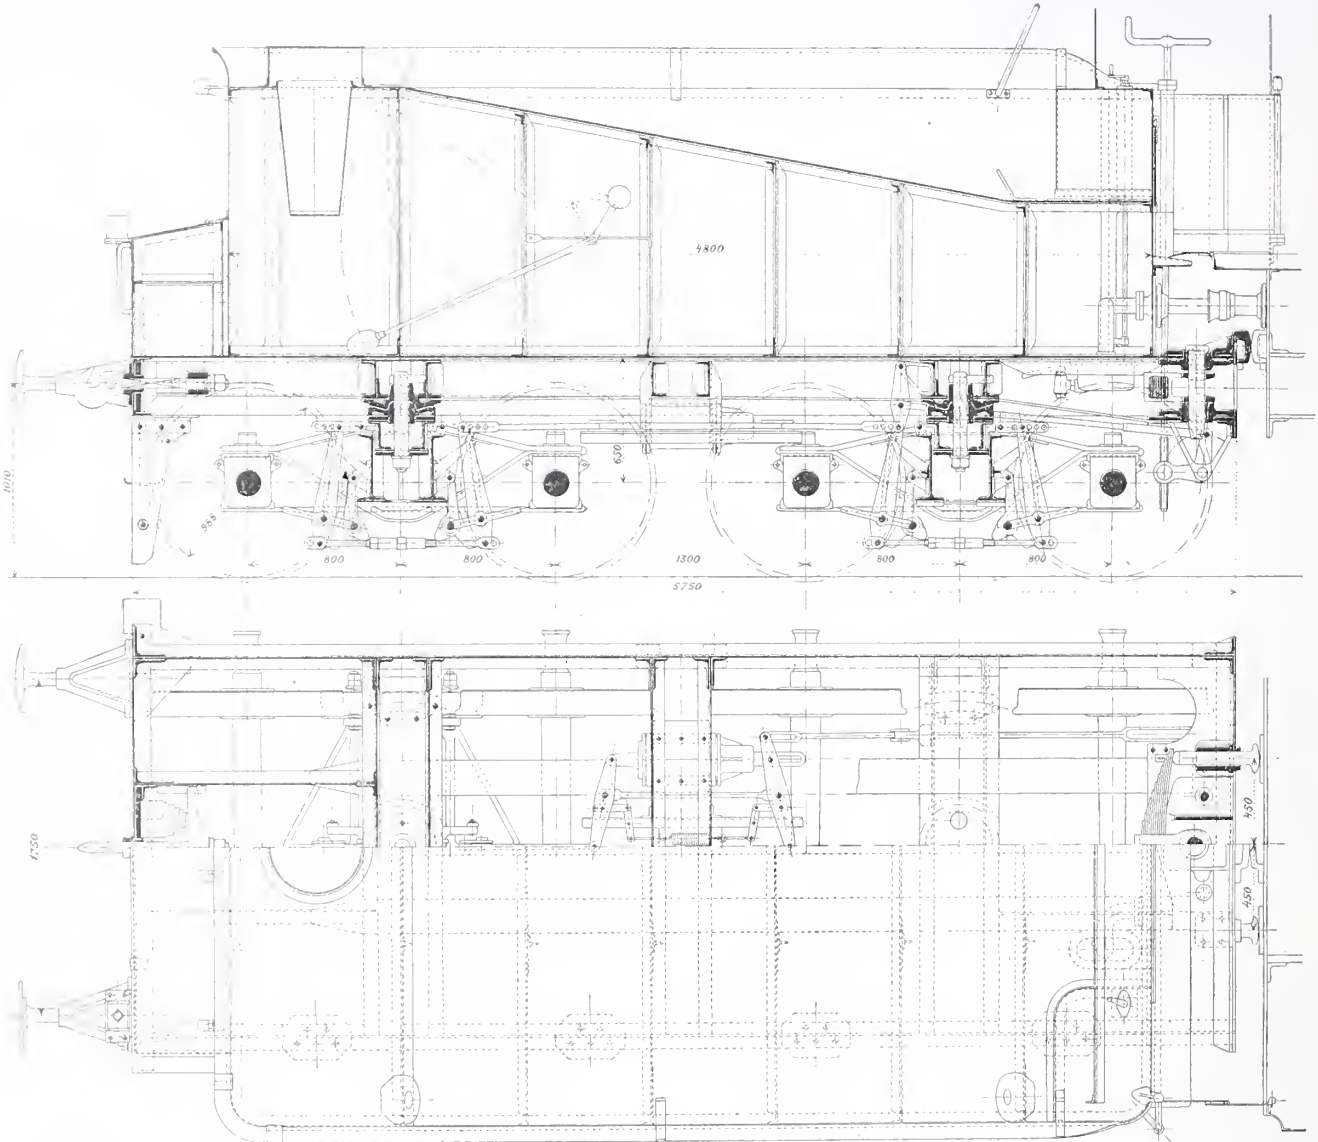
Aufriss, Grundriss und Längsschnitte des Tenders. — Masstab 1 : 40.
